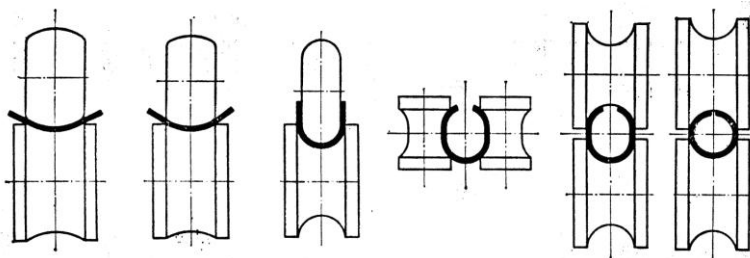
Схема формування смуги в трубну заготівку
